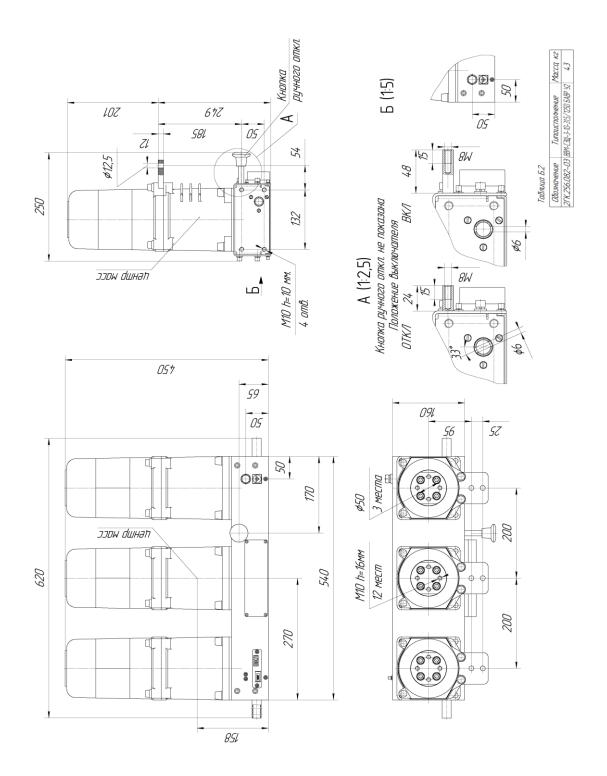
Габаритные, присоединительные и установочные размеры выключателя типа ВВМ-СЭЩ-3-10-31,5/1250 БАВР У2
